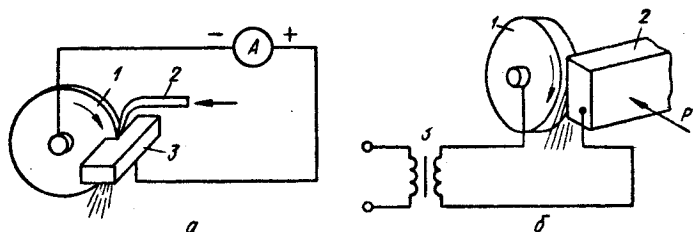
Схема анодно-механічного відрізування заготовки (а) і електроконтактної обробки (б)
